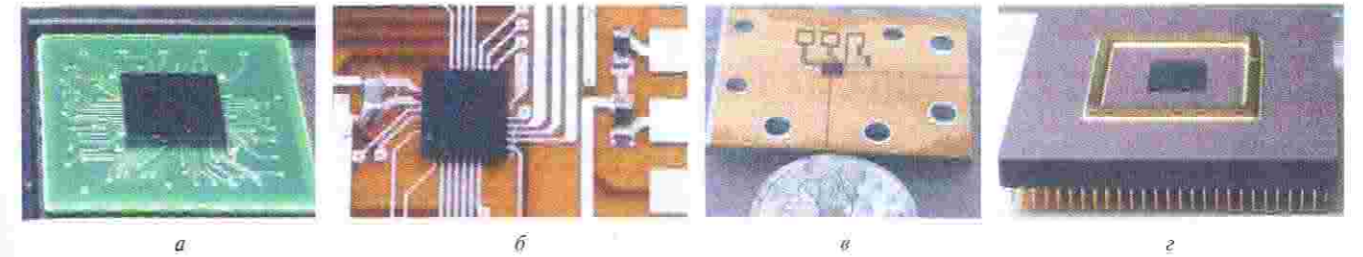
Примеры сборки: а — кремний на стеклотекстолитовую плату; б — кремний на полиимидную плату; в — сапфир на алюмооксидную плату; г — кремний в металлокерамический корпус
